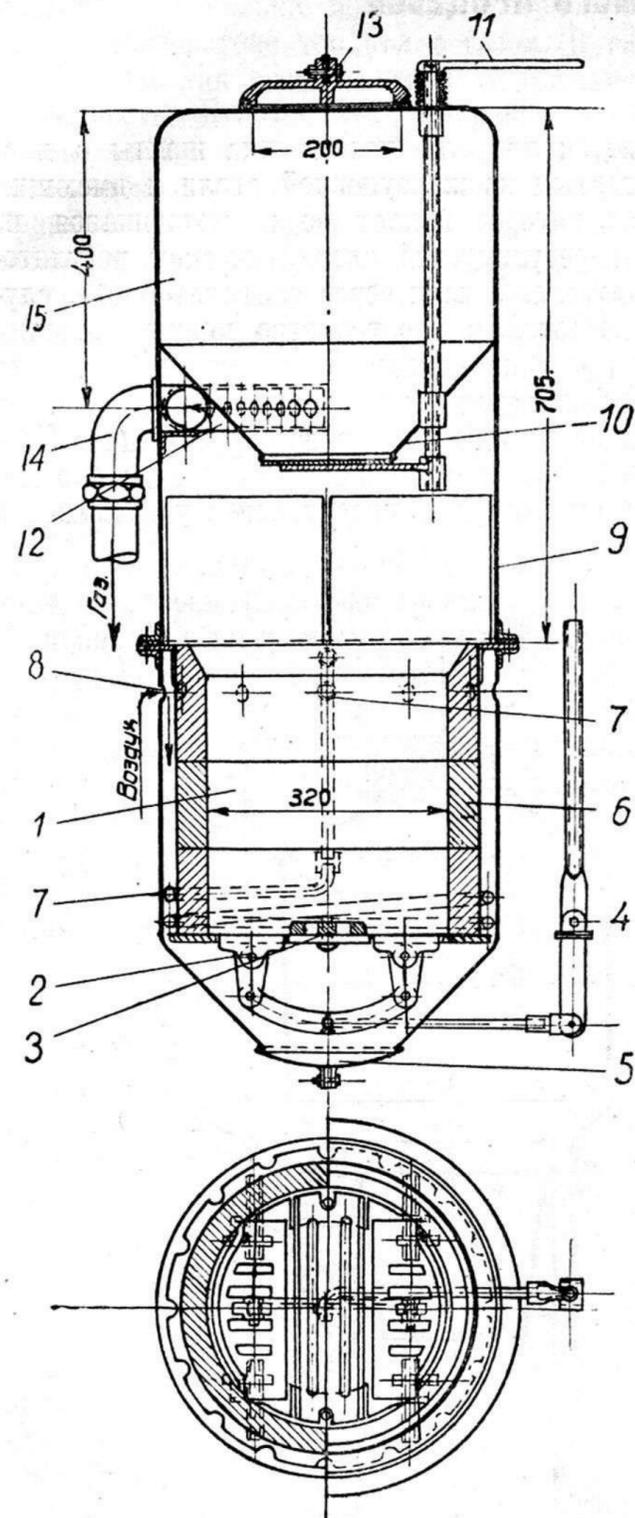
Газогенератор проф. Наумова. 1—топливник; 2—качающийся колосник; 3—неподвижный колосник; 4—рукоятка для встряхивания колосников; 5—зольниковый люк; 6—кольца футеровки; 7—спиральная трубка для подачи воды; 8—отверстия для всасывания воздуха; 9—тепловой асбестовый экран; 10—загрузочный клапан; 11—рукоятка загрузочного клапана; 12—полукольцо газосборной трубы; 13—загрузочный люк; 14—газоотводный патрубок
